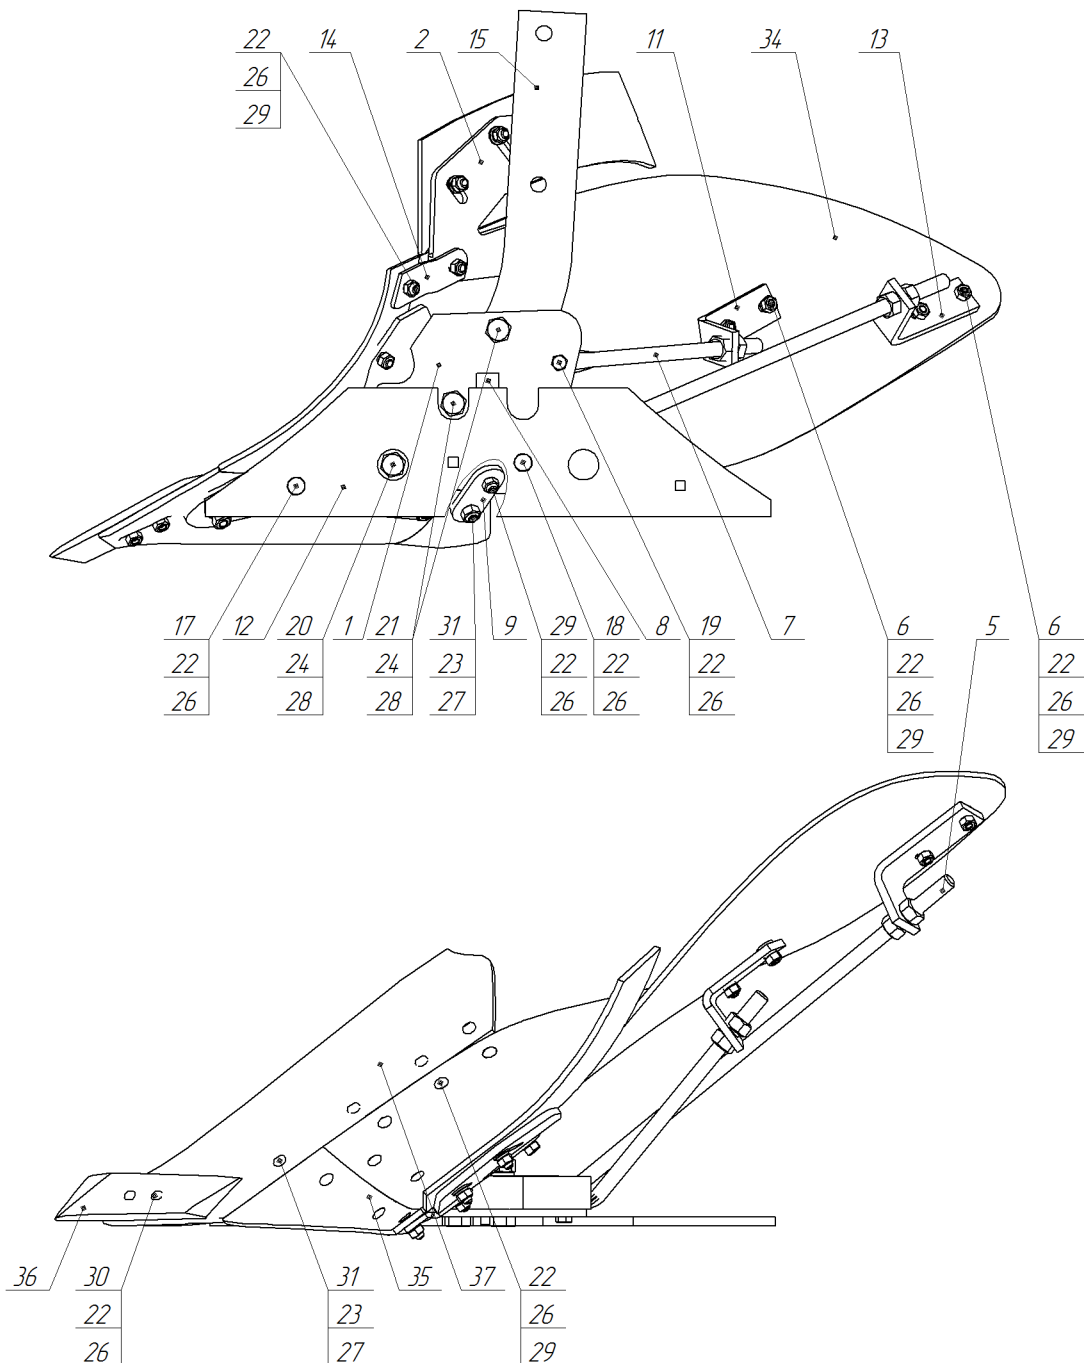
КСО-45 00.00.000 Корпус в сборе правый
